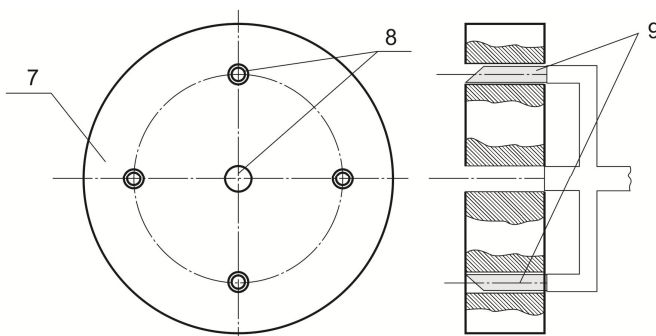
б - Неподвижный жернов с напороустойчивыми трубками
